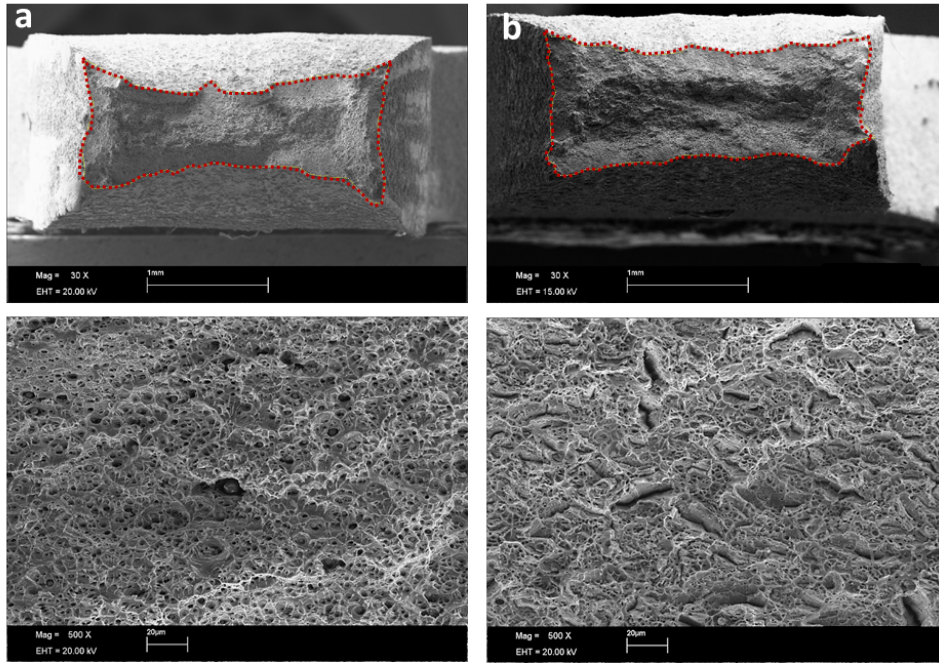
Surfaces de rupture dans l'acier 308L d'éprouvettes de traction à l'état a- brut de soudage; b- détensionné.
